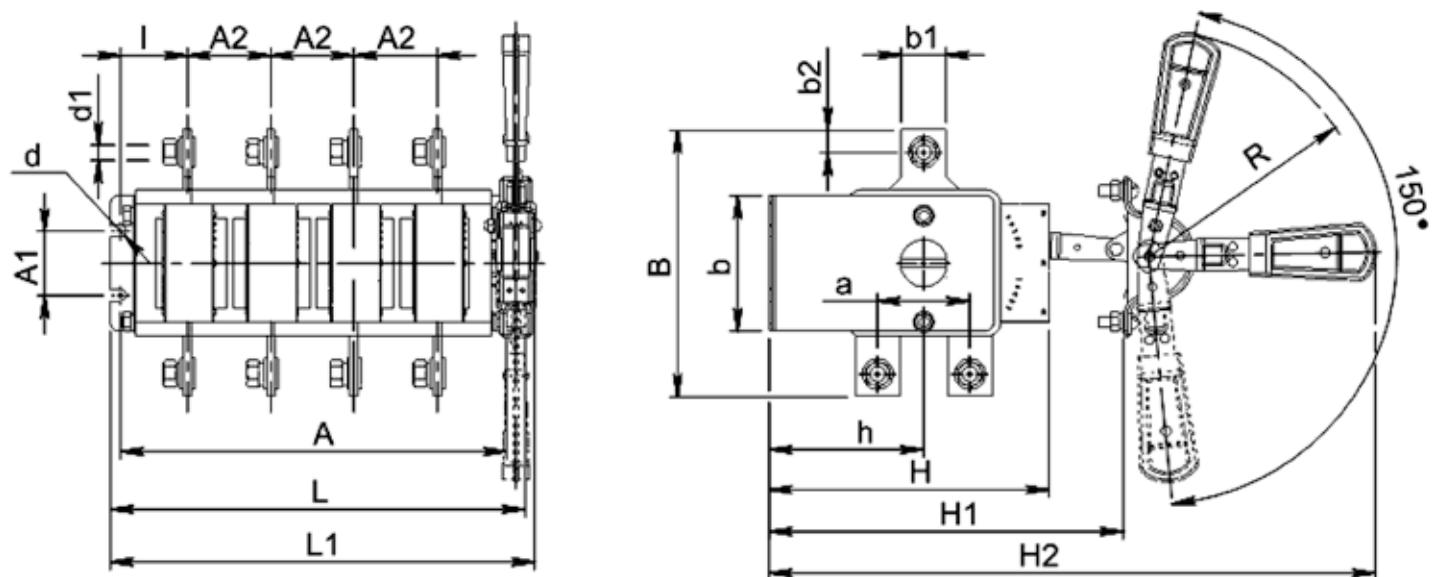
Выключатель-разъединитель на два направления 4-полюсный с передней смещенной рукояткой
